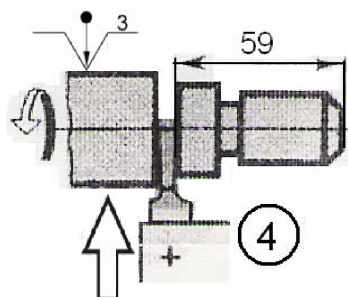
Отрезание заготовки длиной 59 мм
